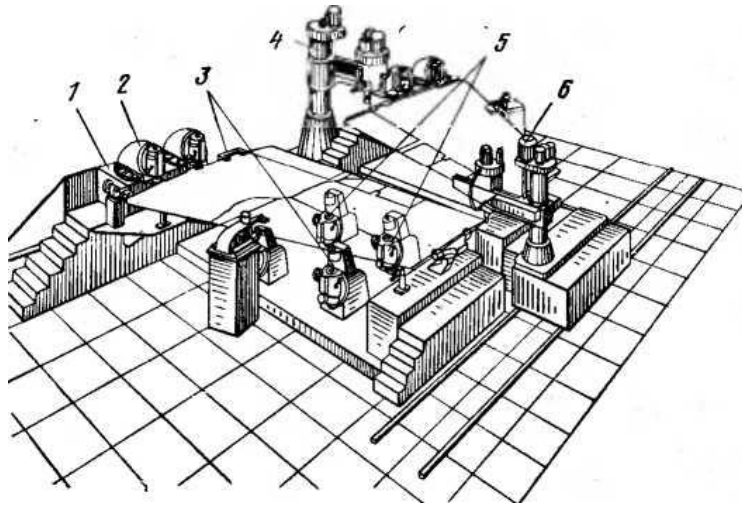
Агрегатно-разделочный стенд крыла:
